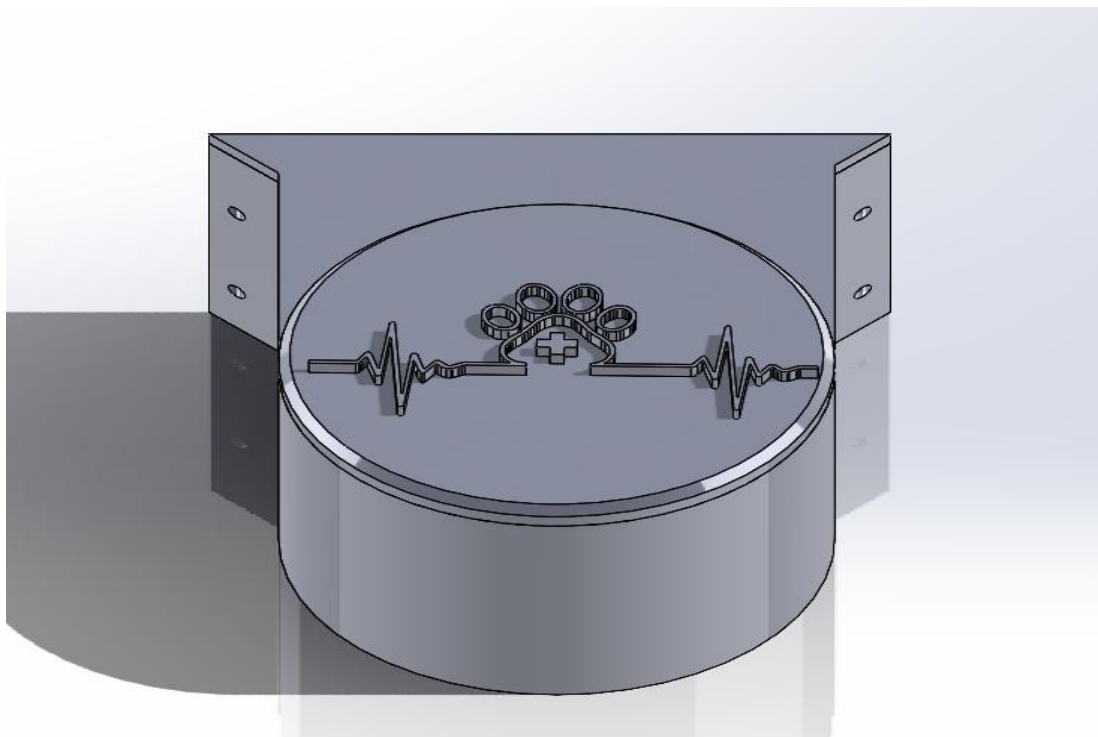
Ensamblaje Dispensador Automático (Alzado).
